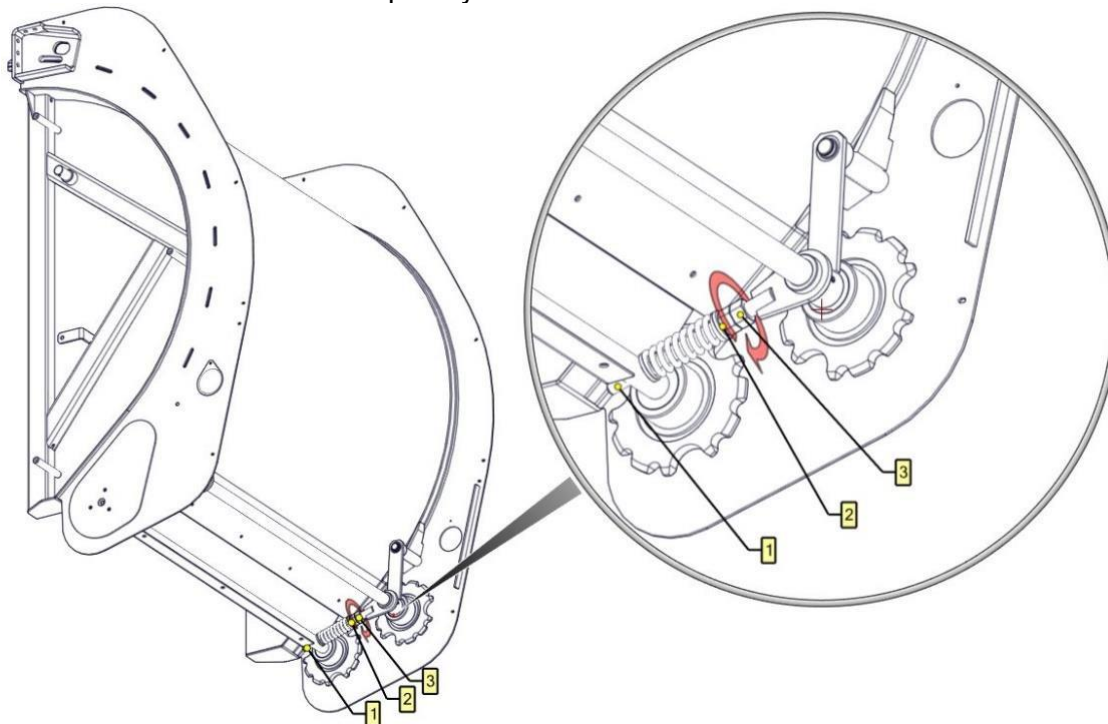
Регулировка натяжения цепного пруткового транспортера пресс-подборщика Z587/1
